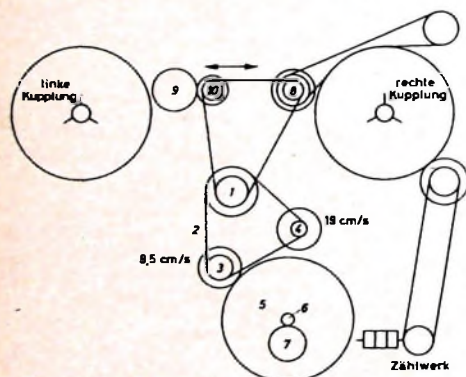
Prinzip des Laufwerks mit Motor 1, Flachriemen 2, Reibrad 3, Reibrad 4, Schwungscheibe 5, Tonwelle 6, Gummiandruckrolle 7, Zwischenrad für Vorlauf 8, Zwischenrad für Rücklauf 9 und Reibrad 10
